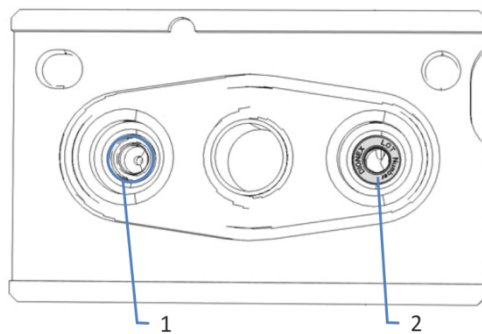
Pumpenkopf (links: ohne Kolbendichtung; rechts: mit Kolbendichtung)
